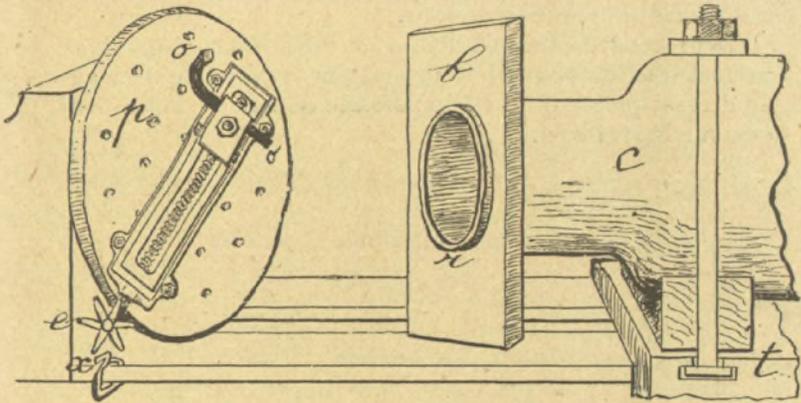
Installation d'un chariot porte-outil sur le plateau du tour pour dresser une bride de cylindre.
